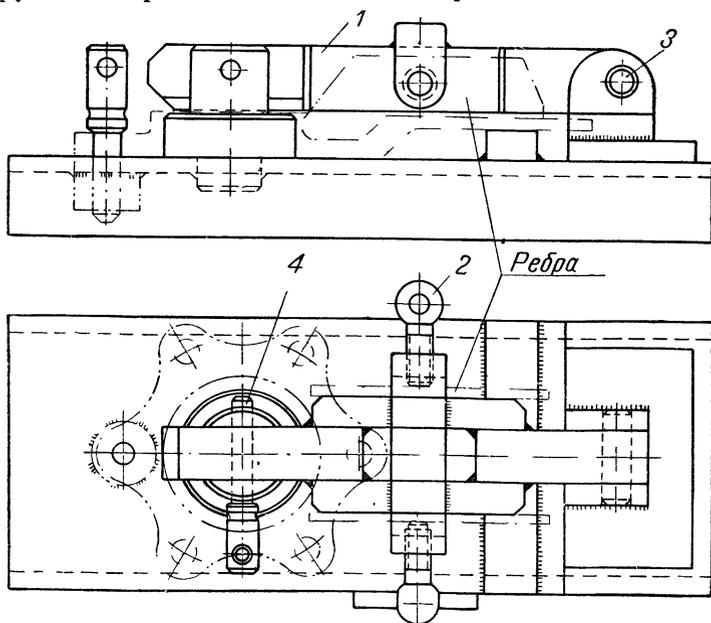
Приспособление для сборки и прихватки кронштейна.
